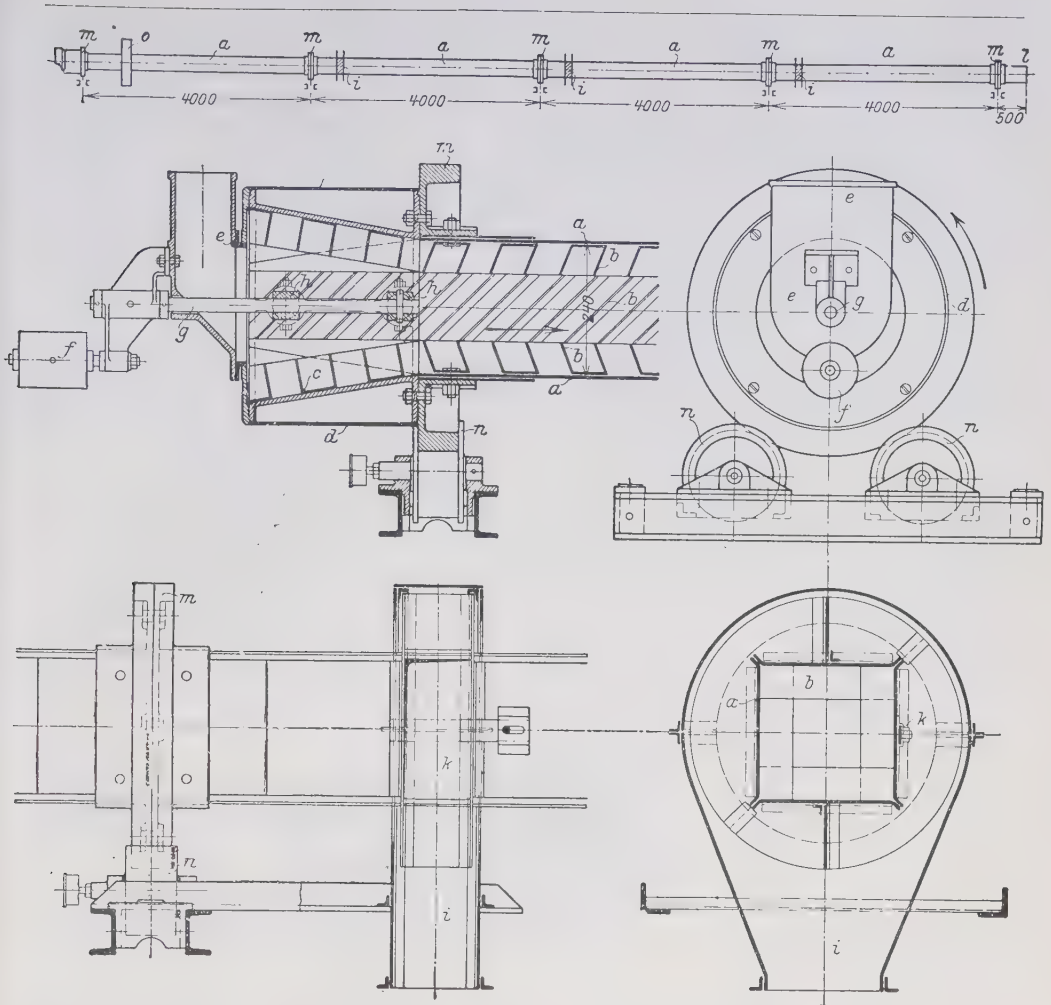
Transportador de canal cuadrada sistema Suesz; disposición general y detalles constructivos
